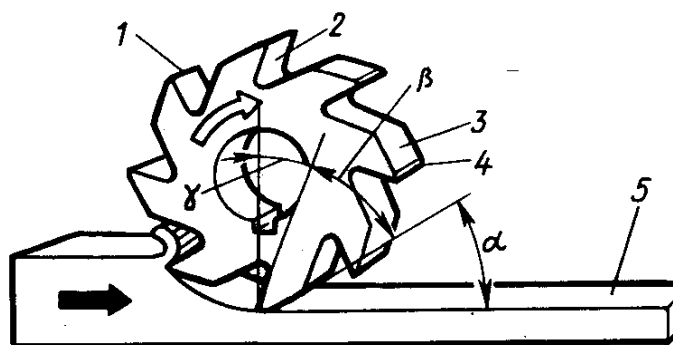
Геометрические элементы режущей части цилиндрической фрезы: 1 – режущая кромка; 2 – передняя поверхность; 3 – задняя поверхность; 4 – ленточка; 5 – обработанная поверхность заготовки
